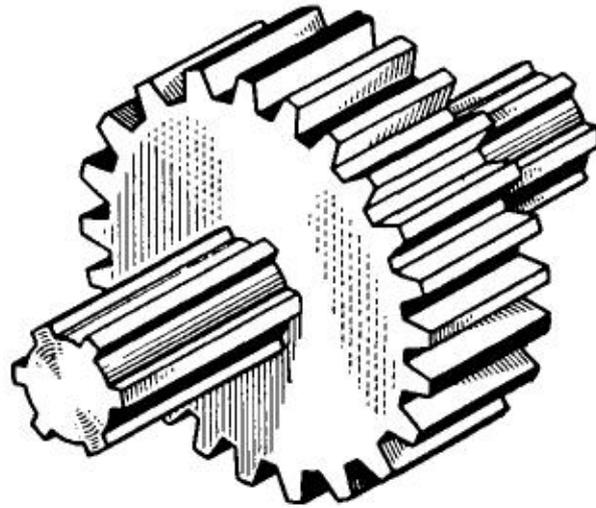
Загальний вигляд шліцьового з'єднання.
